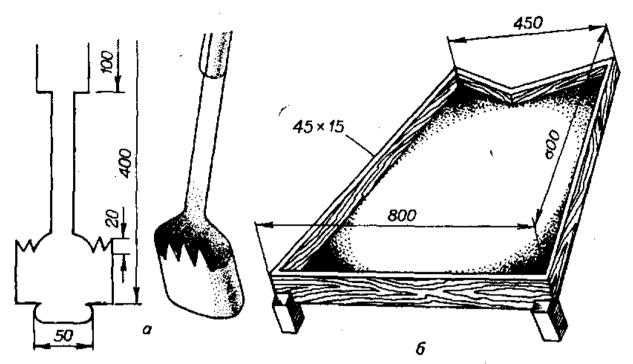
Приспособления для сбора ягод крыжовника: а - ковш-гребенка; б - лоток. Фото М. Г. Крюгера.
